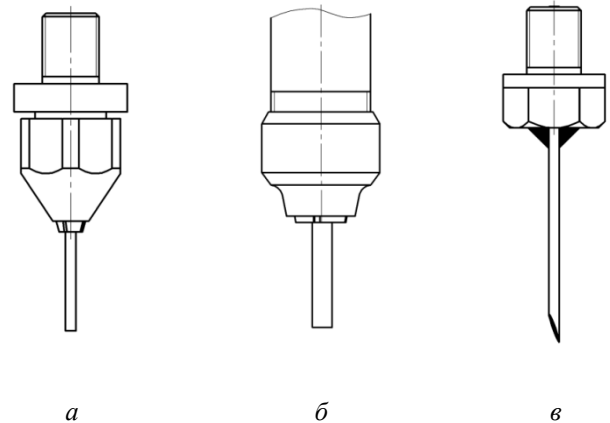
Пассивные рабочие инструменты для размерной обработки с цанговыми зажимами
